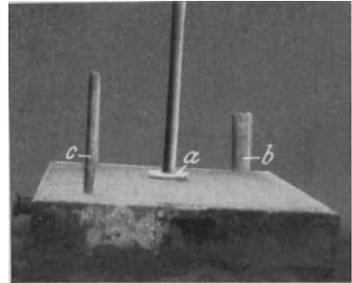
Aufstampfform fertig zum Aufsetzen des Oberkastens.
